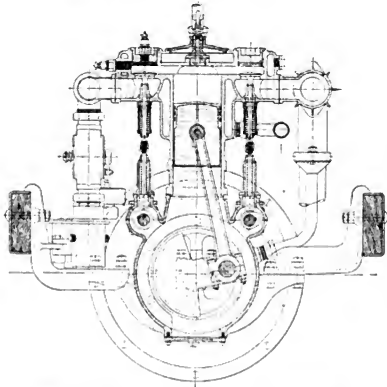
Sechszylinder-Hexe-Motor; im Querschnitt.
